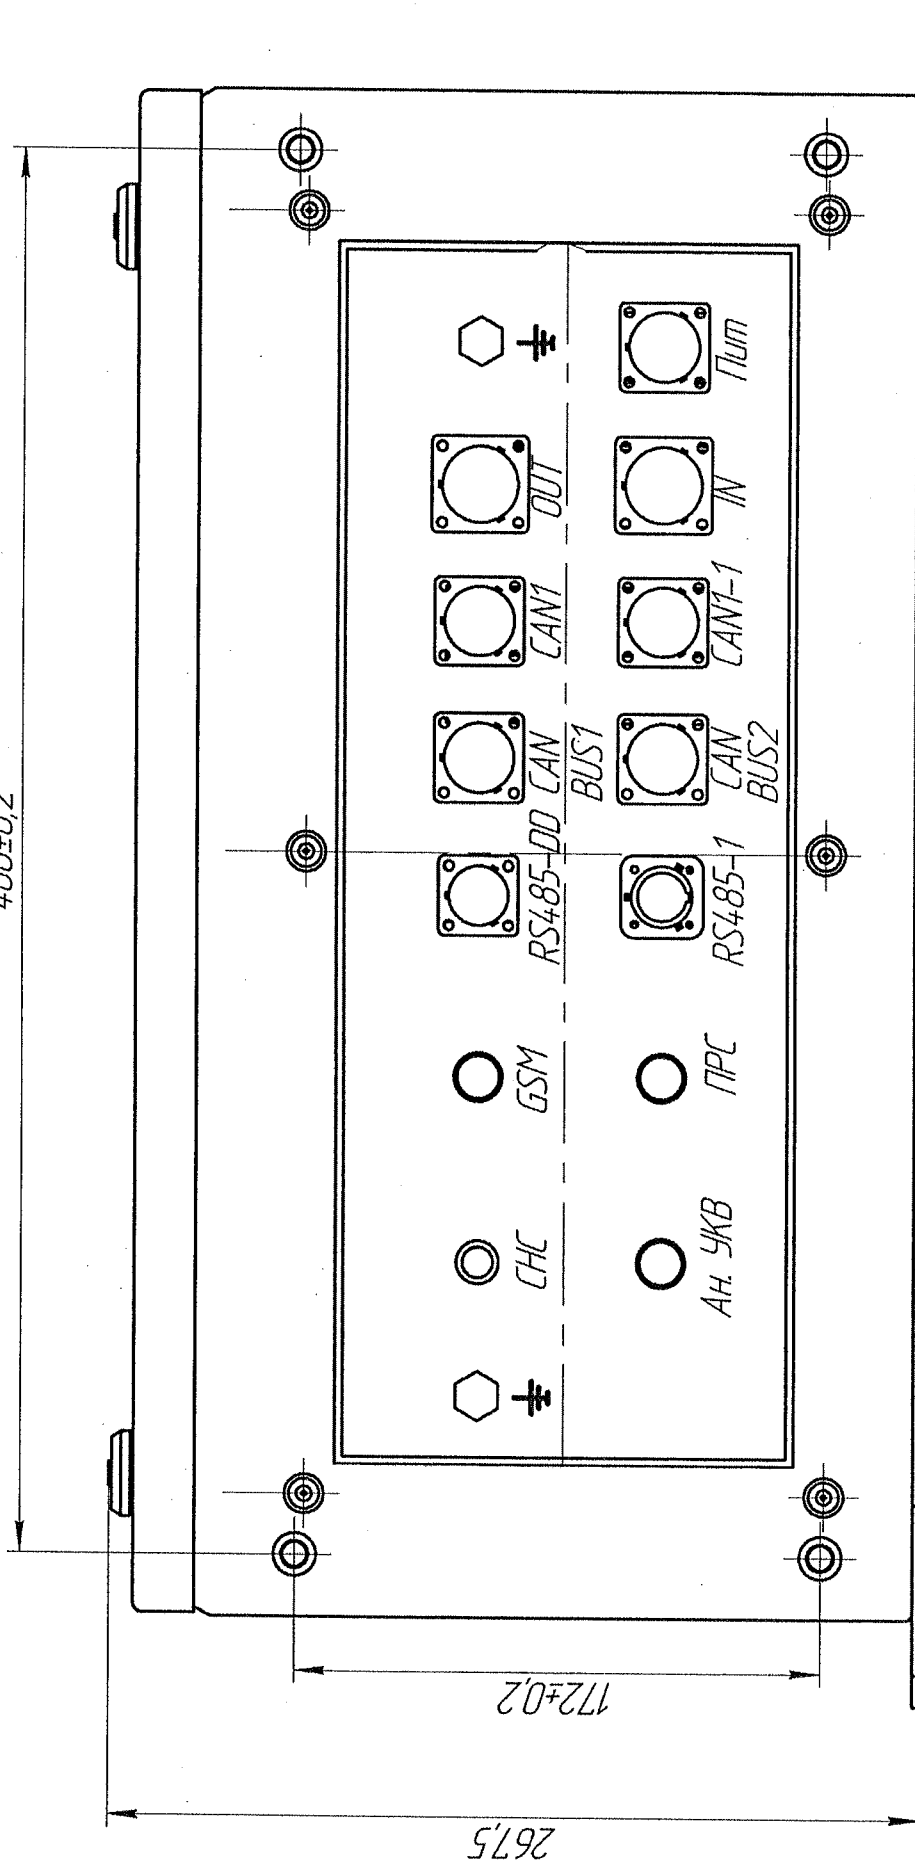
Внешний вид (вид снизу) и габаритные размеры.
